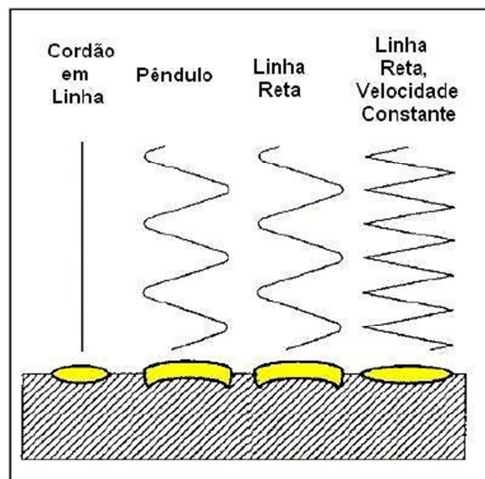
Técnicas básicas de oscilação e configurações dos cordões de solda
